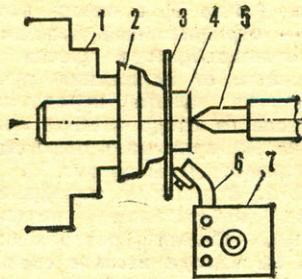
Схема выдавливания диска колеса на токарном станке: 1 — патрон; 2 — оправка; 3 — заготовка; 4 — упор; 5 — вращающийся центр; 6 — ролик для выдавливания; 7 — резцедержатель.
